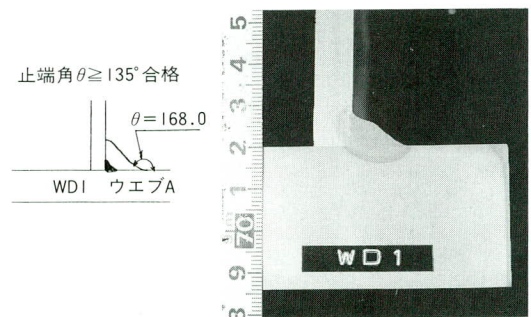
端部ダイヤフラムC2溶接断面マクロ試験
